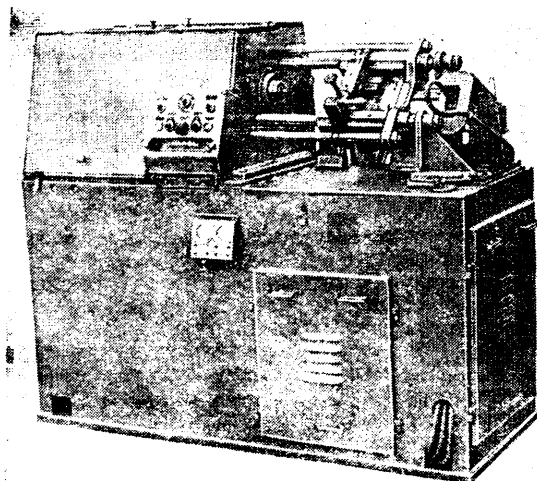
Внешний вид универсального станка сварки трением типоразмера I (ПСТ-1,5).
